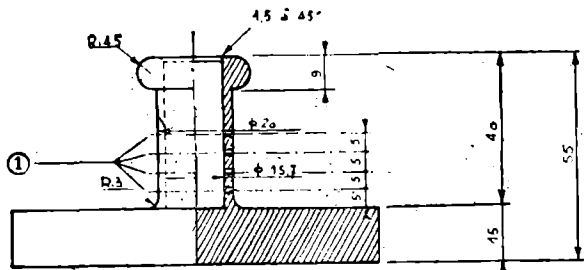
Cilindro hueco de bronce cerrado por un lado (planta y sección vertical). (Dimensiones en mm.)
